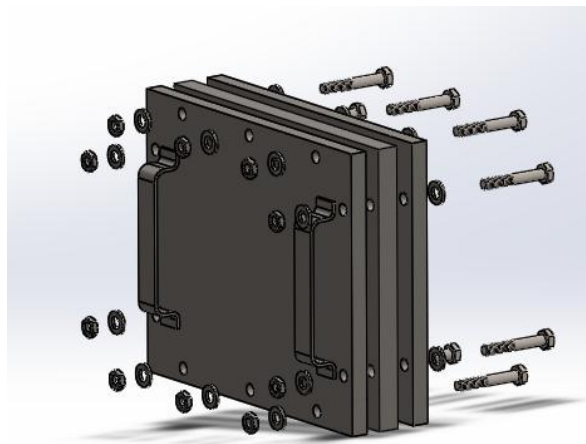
Componentes del molde de curación para probetas a compresión.
